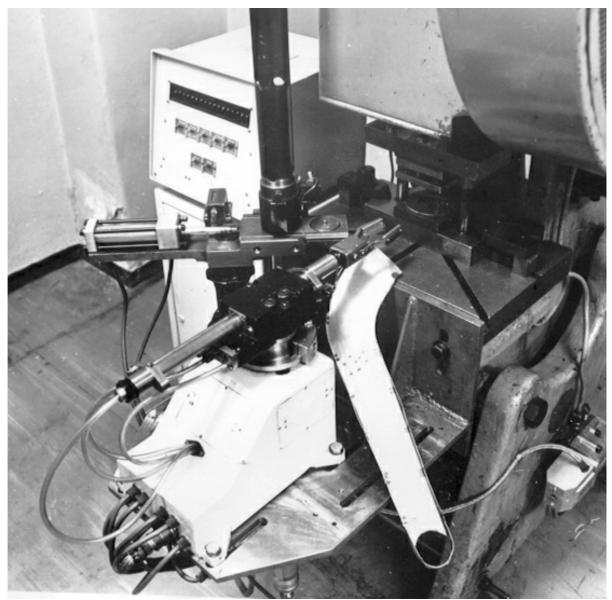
Робот МП-9С на обслуживании пресса холодной штамповки. Справа устройство группового управления и магазин заготовок (вертикальный) с пневматическим толкателем. Слева — лоток для сбрасывания деталей в магазин.
